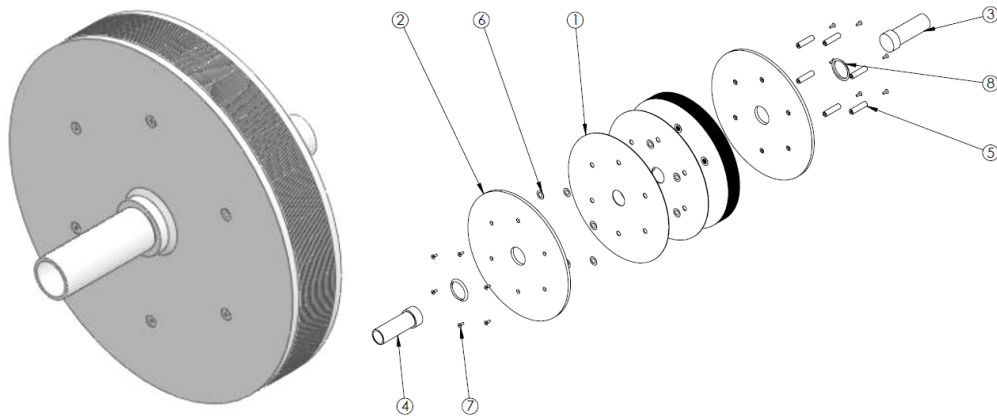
Ilustrační fotografie rotoru – hřídel a rotor se sadou disků [10].
